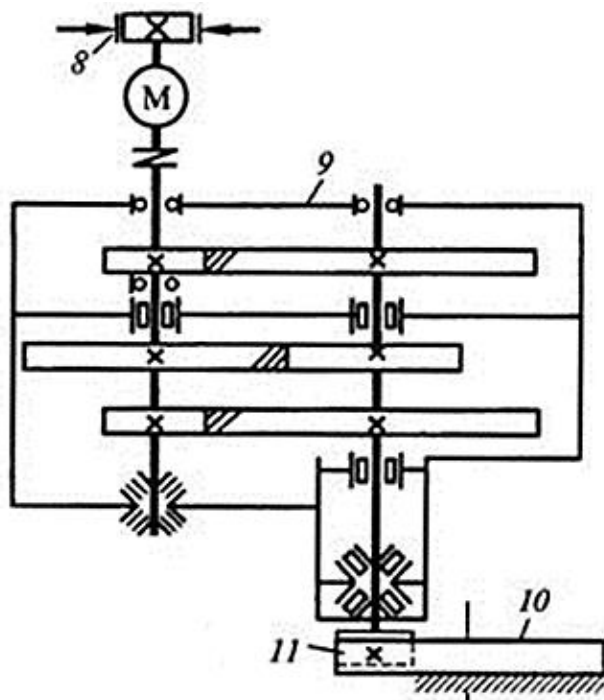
Кинематическая схема механизма поворота: 8 - тормоз; 9 - трехступенчатый редуктор; 10 - зубчатый венец; 11 - выходная шестерня
